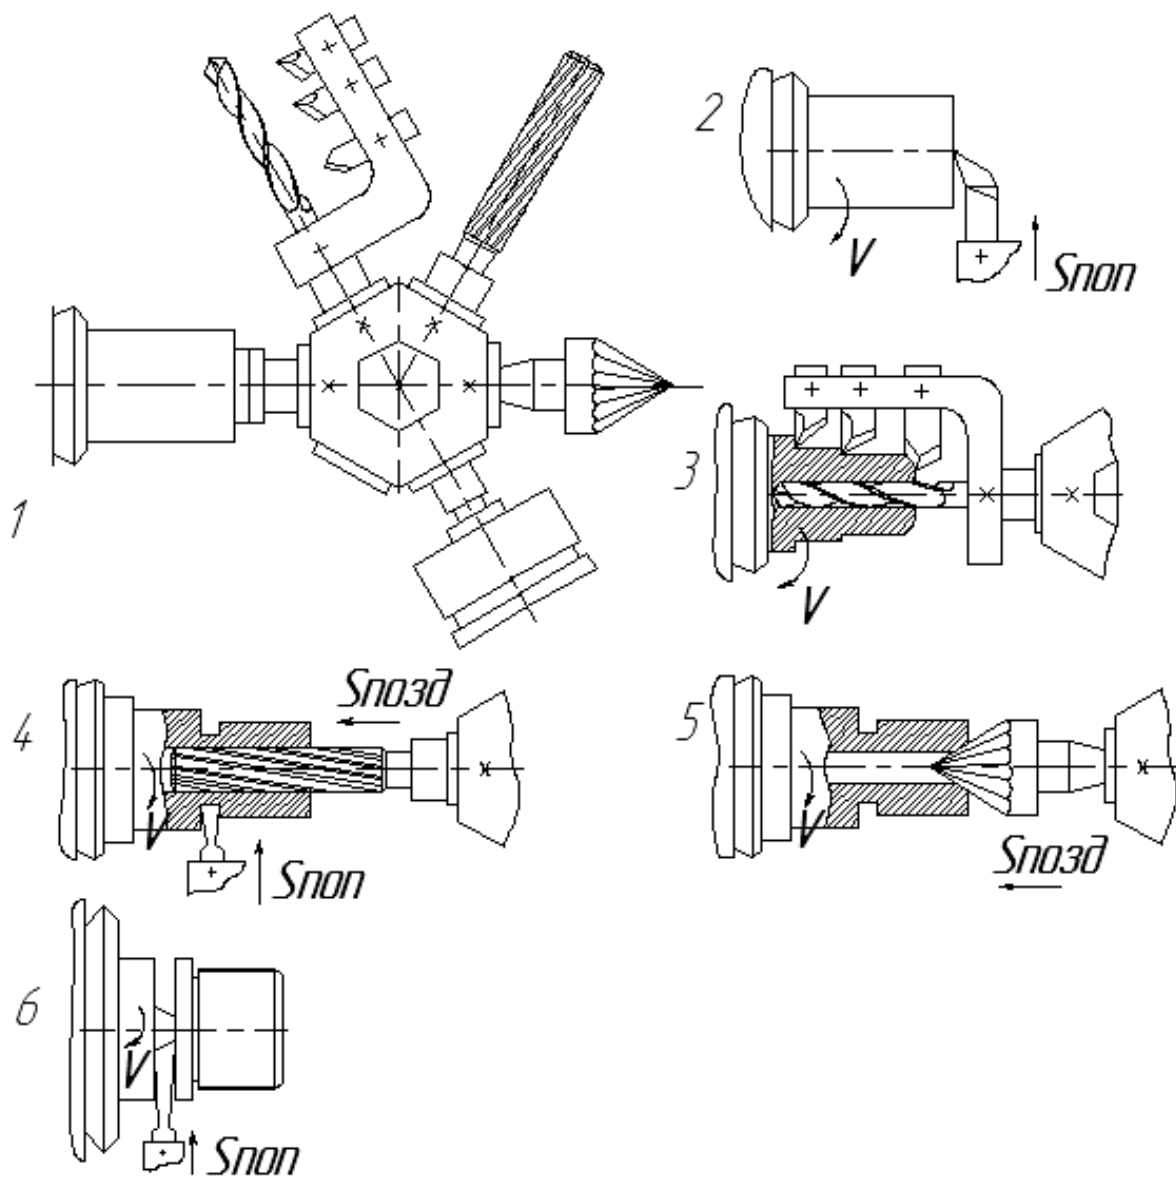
Схеми обробки поверхонь заготовок на токарно-револьверних верстатах
